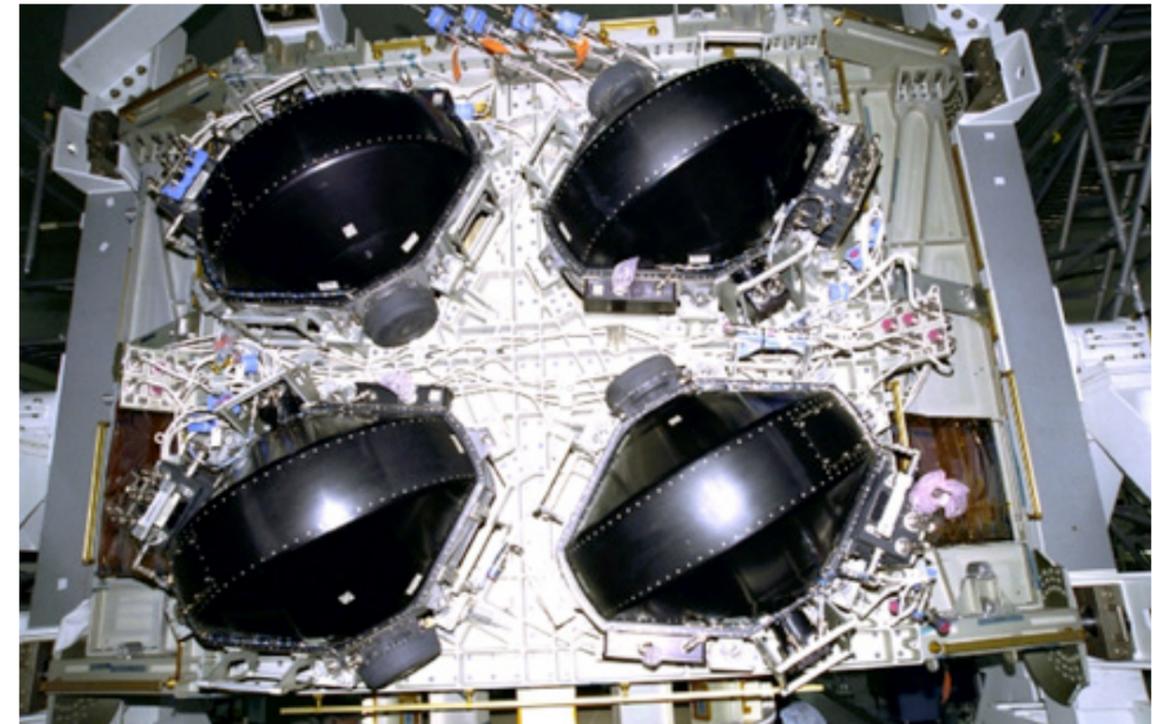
Photo du CMG assemblé sur la poutre central de l'ISS
